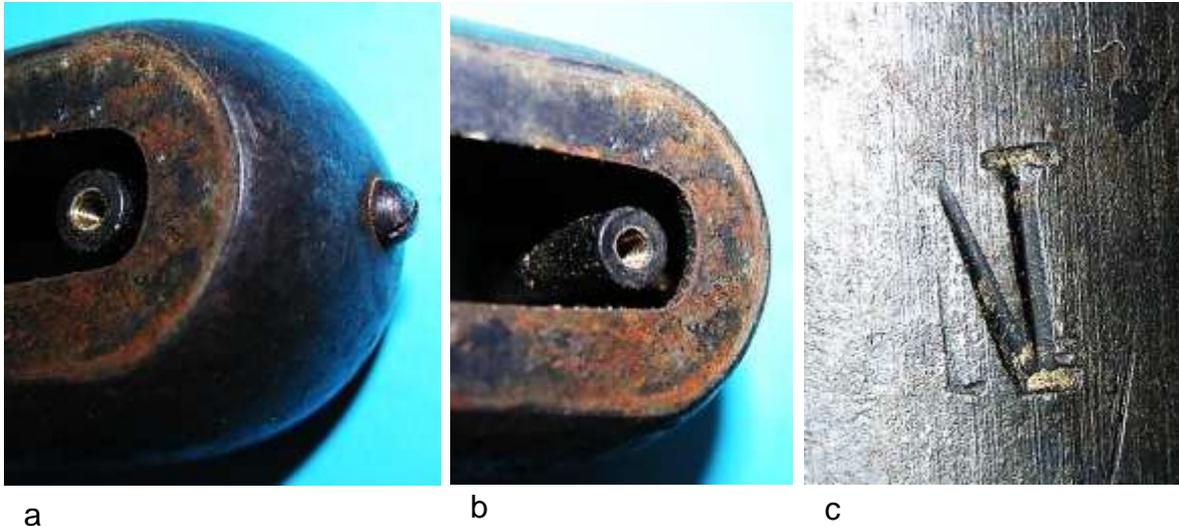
Montagehilfen: a) und b) Gewindehülse zur Befestigung der Pollückenbleche, c) Markierung des Nordpols
